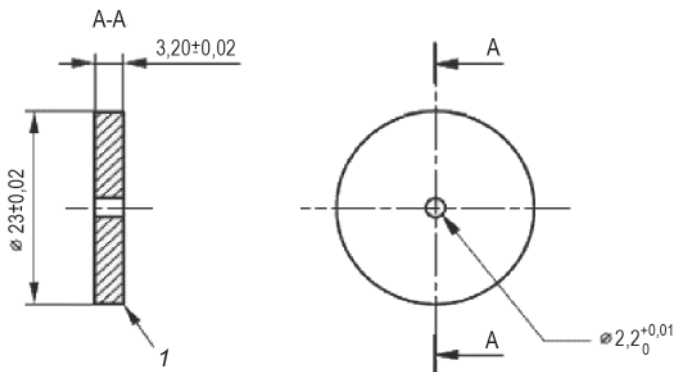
Деталь 6 – Диафрагма с отверстием G:
